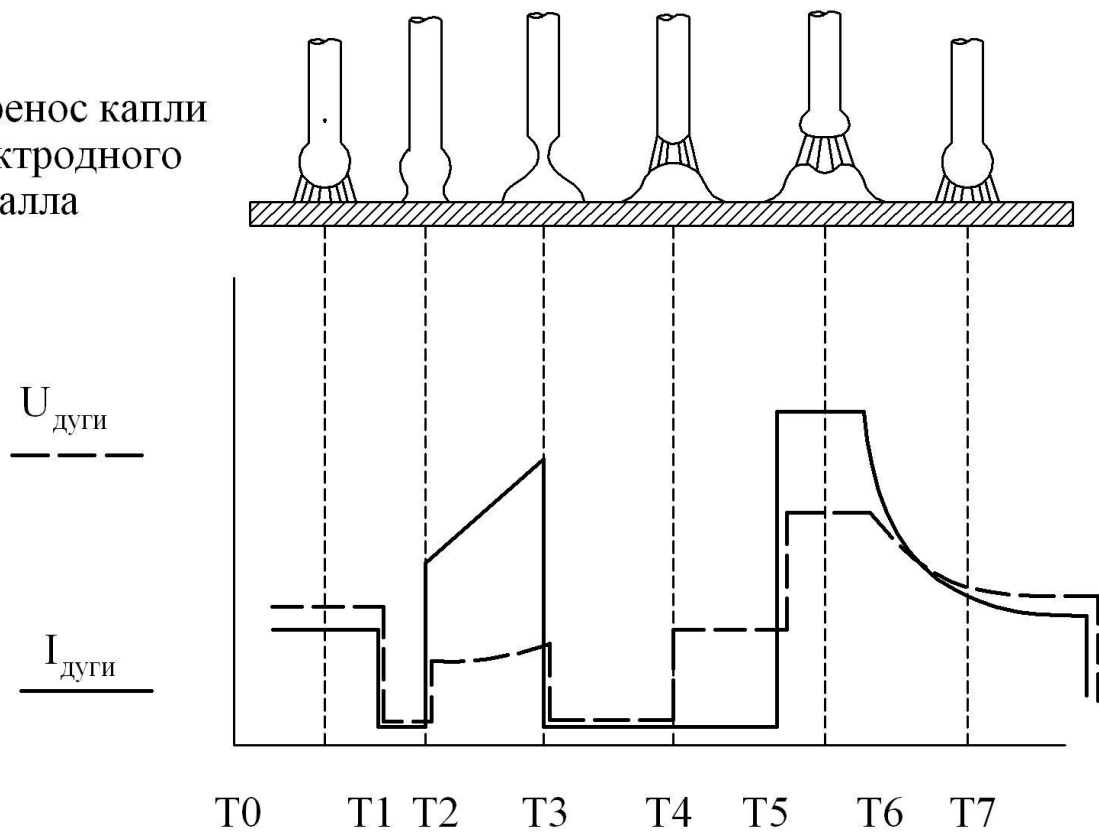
Осциллограммы сварочного тока и напряжения при полуавтоматической сварке методом STT
